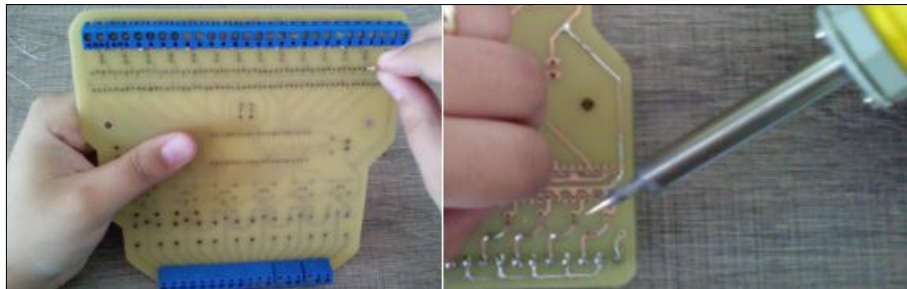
Montagem e soldagem dos componentes eletrônicos na placa
